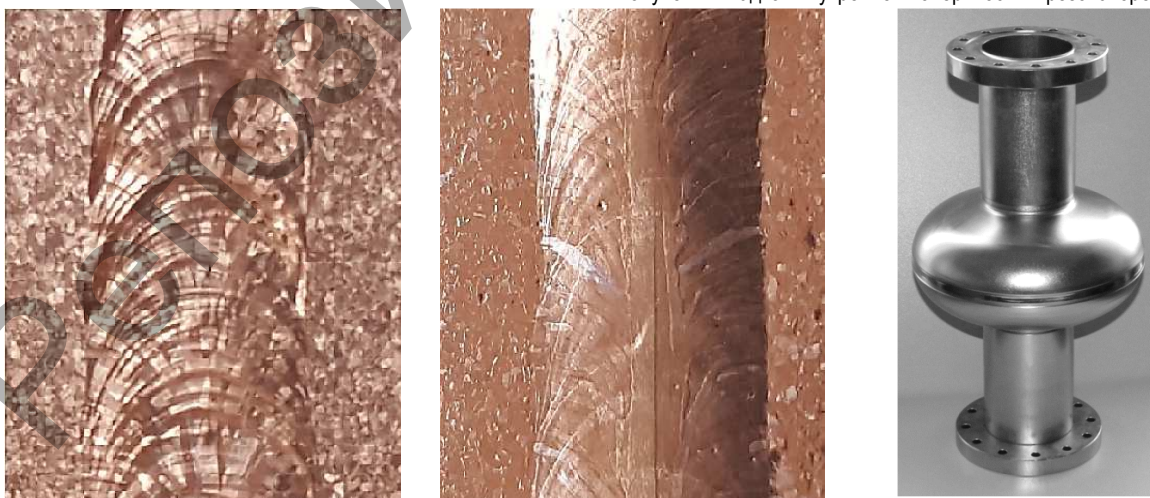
Образцы и изделие, полученные ЭЛС: обратная поверхность сварных соединений меди М1, изготовленных с использованием различных режимов, $\times 10$ (а, б) и эллиптический СВЧ резонатор из особо чистого ниобия (в)
